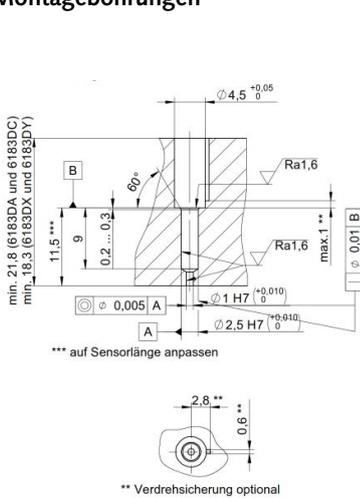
Montagebohrung für Einbau mit Distanzhülse
